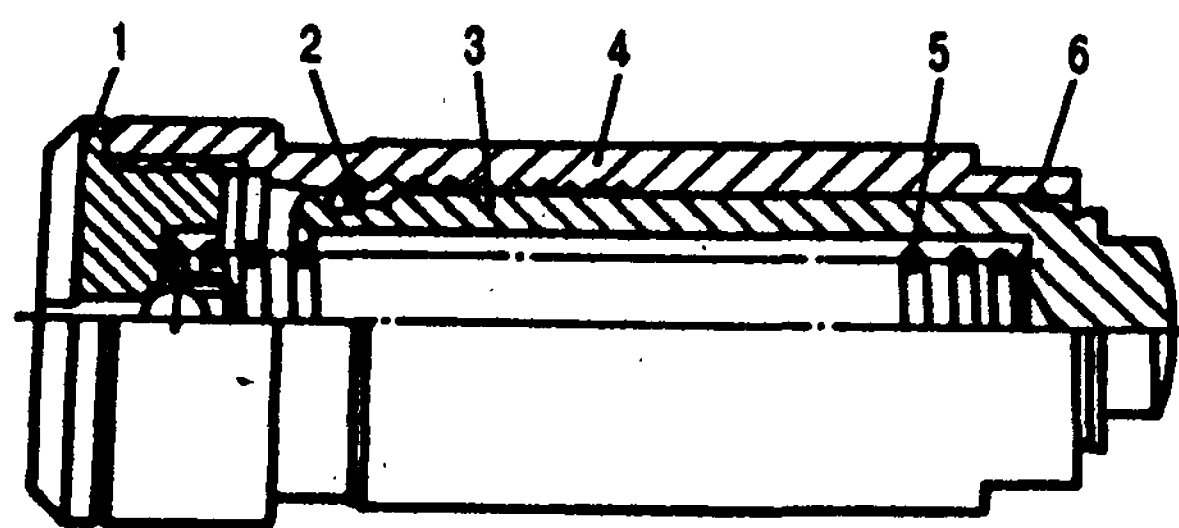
Гидронатяжитель в сборе: 1 - корпус клапана в сборе; 2 - кольцо запорное; 3 - плунжер; 4 - корпус; 5 - пружина; 6 - кольцо стопорное
